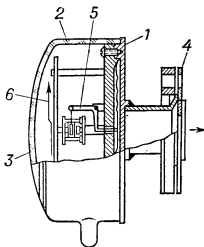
Мембранный вакуумметр: 1 — мембрана; 2 — корпус; 3 — передняя прозрачная поверхность вакуумметра; 4 — присоединительный фланец; 5 — система рычагов; 6 — стрелка.
